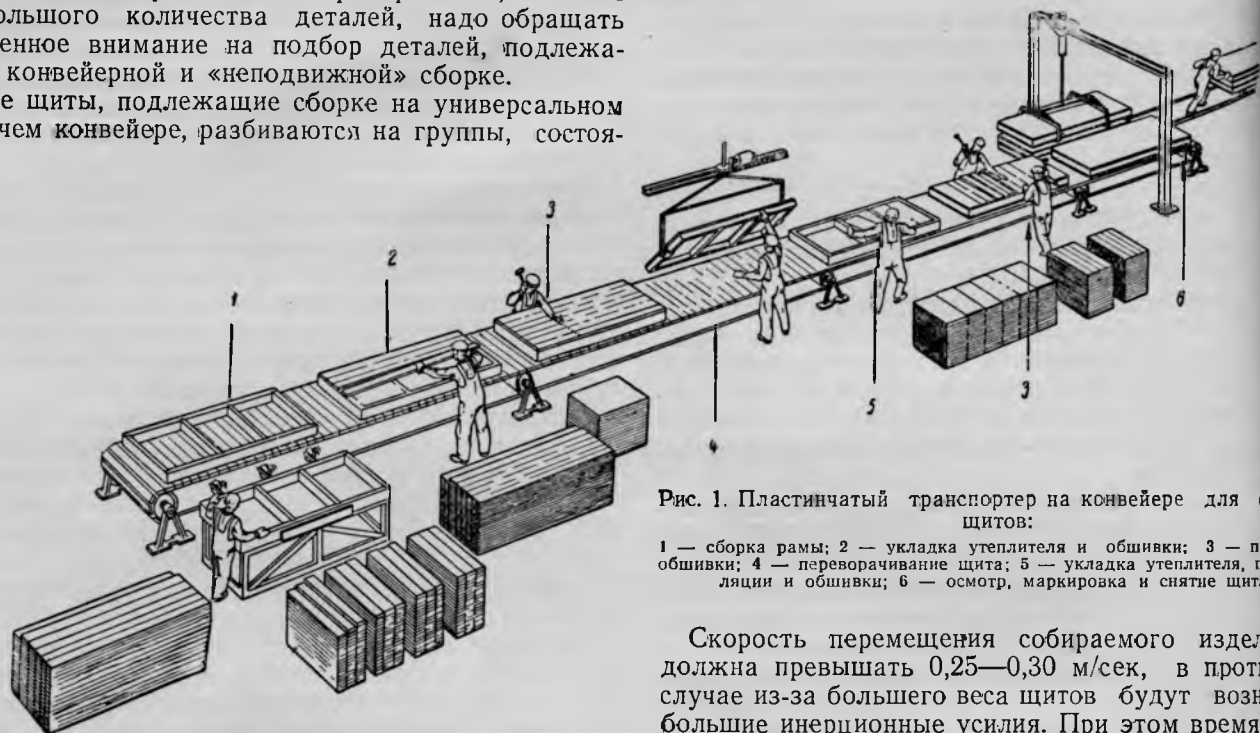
Пластичатый транспортер на конвейере для сборки щитов:
